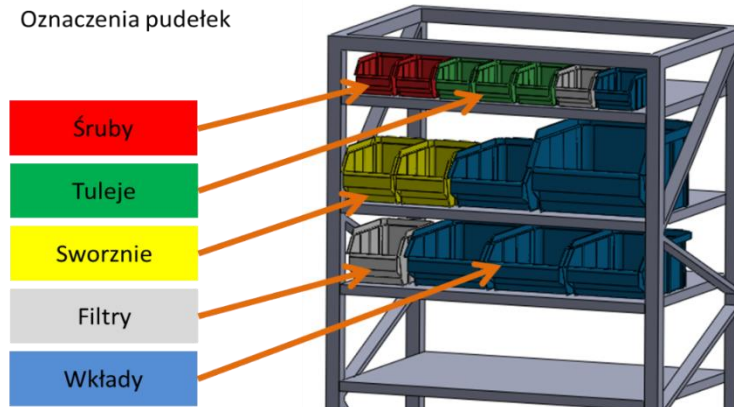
Wizualizacja sposobu przechowywania elementów łącznych; oprac. własne
